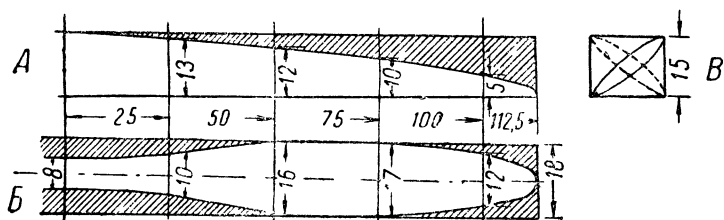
Винт (шаблон): А — вид сбоку; Б — вид сверху; В — вид с торца
